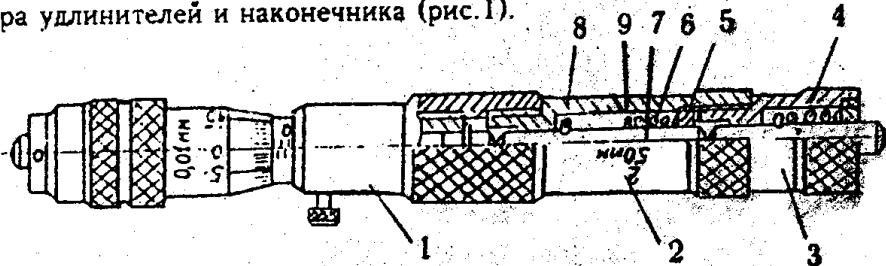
Нутромер НМ-1250: 1 – микрометрическая головка; 2 – удлинитель; 3 – наконечник; 4 – корпус; 5 – гайка крепежная; 6 – пружина; 7 – стержень измерительный; 8,9 – штифты
